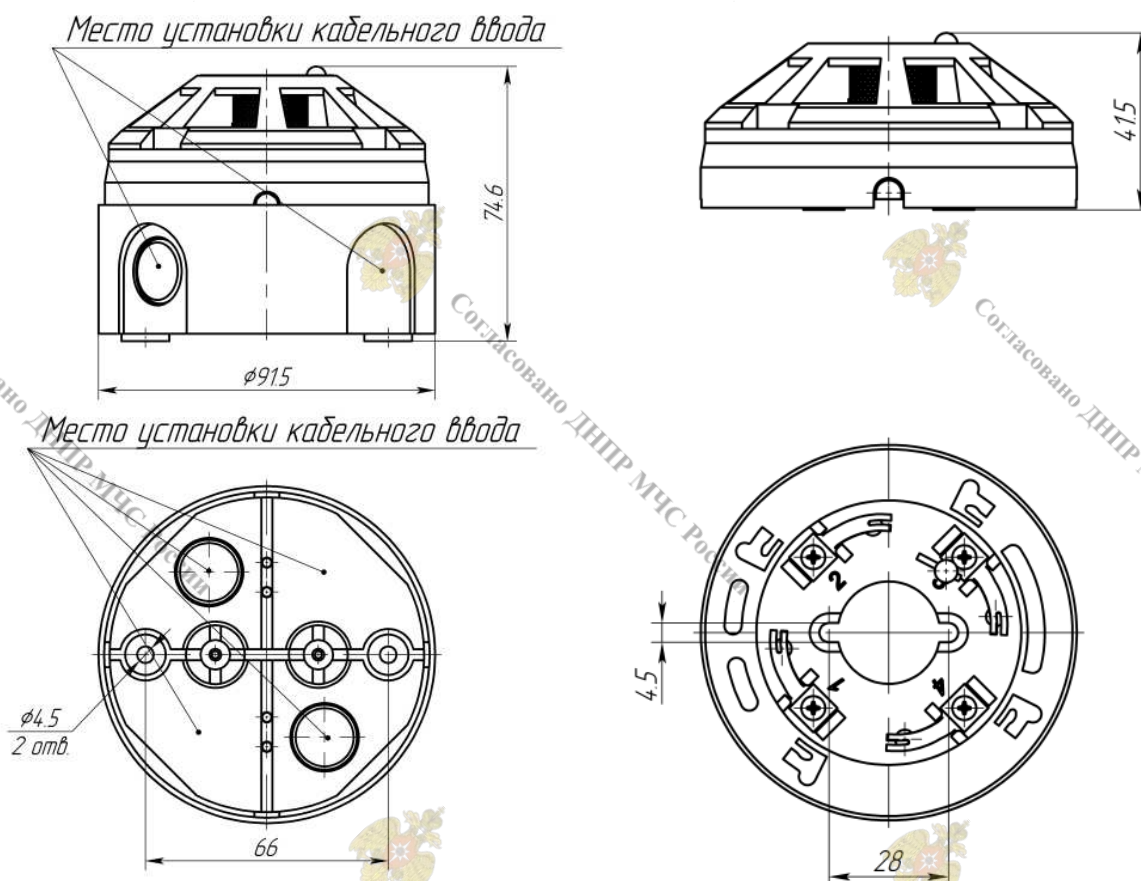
Внешний вид извещателя дымового «ИП 412-1»
